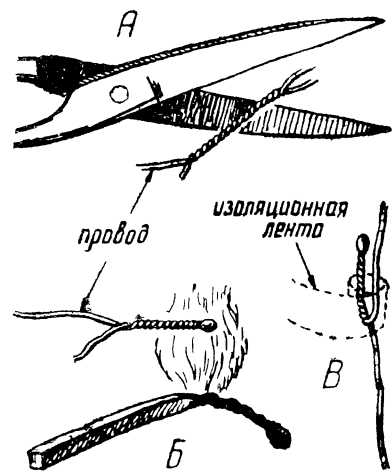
Сварка тонких проводов: А — обрезка скрученных проводов, Б — сварка в пламени спички; В — укладка соединённых сваркой проводов
